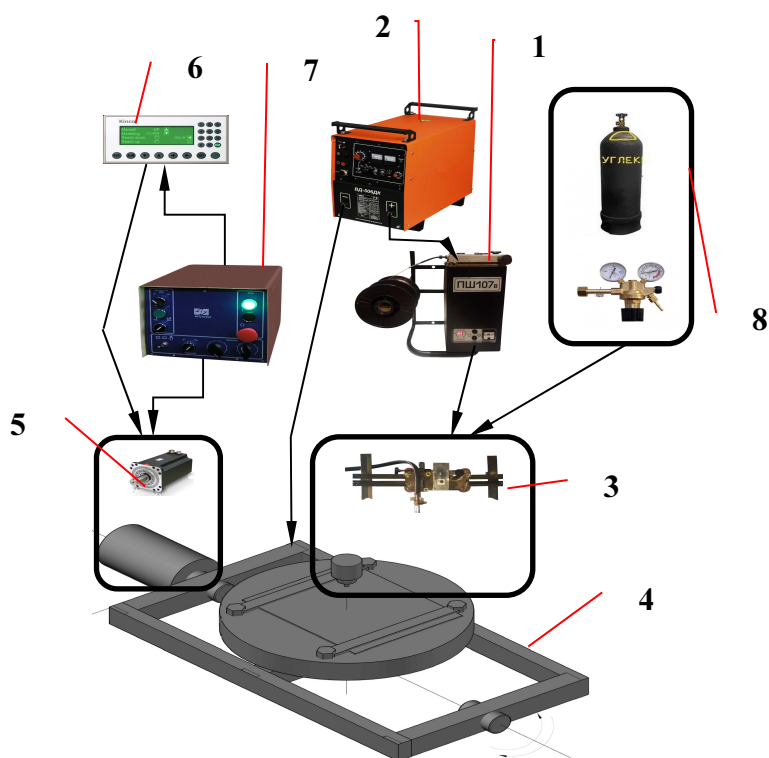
Схема установки для наплавки в среде углекислого газа с колебаниями сварочной ванны
